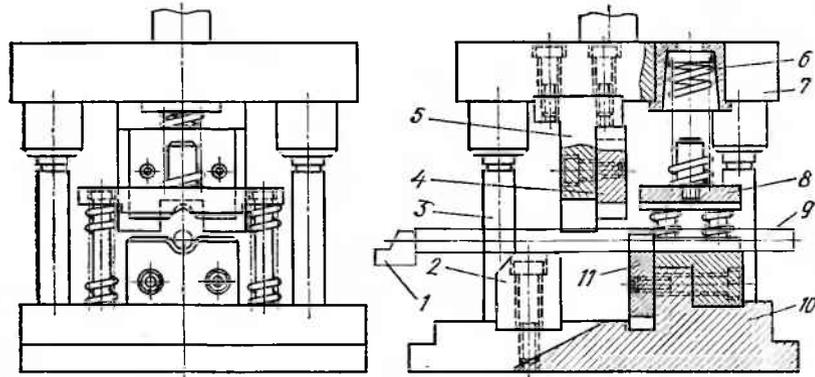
Одноопорный штамп для резки прутков на кривошипном прессе:
